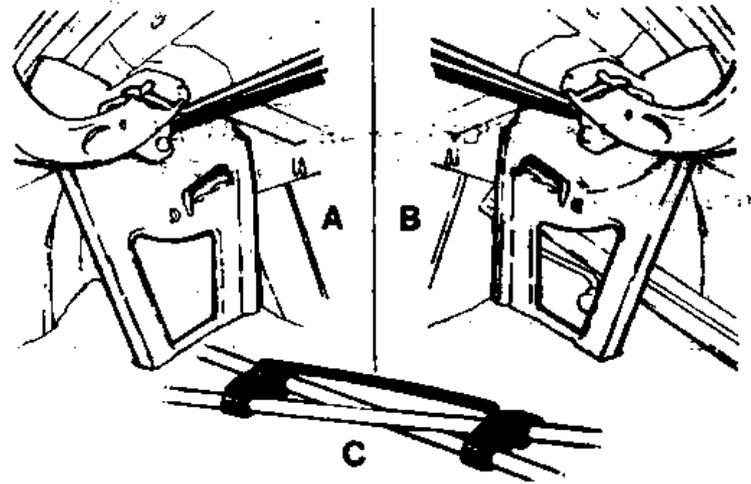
Устройство торсионных штанг крышки багажника (Разд. 15)
